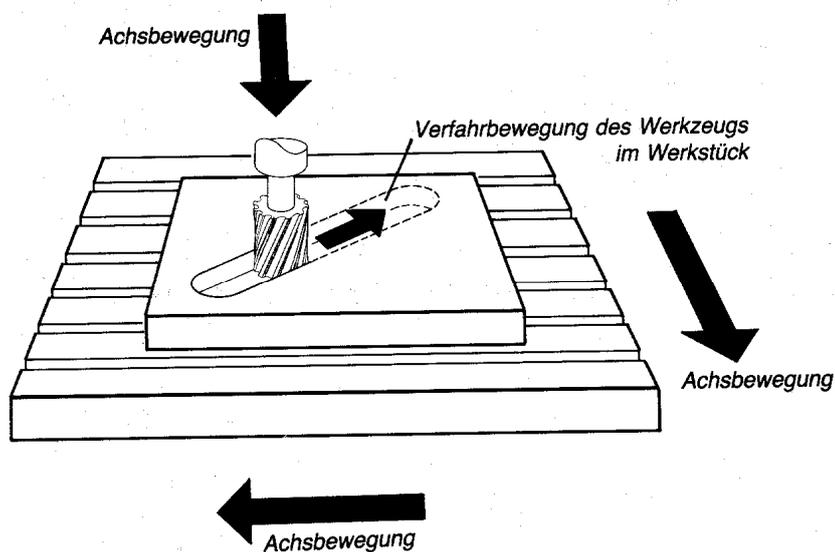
Koordinatenachsen von CNC-Werkzeugmaschinen
